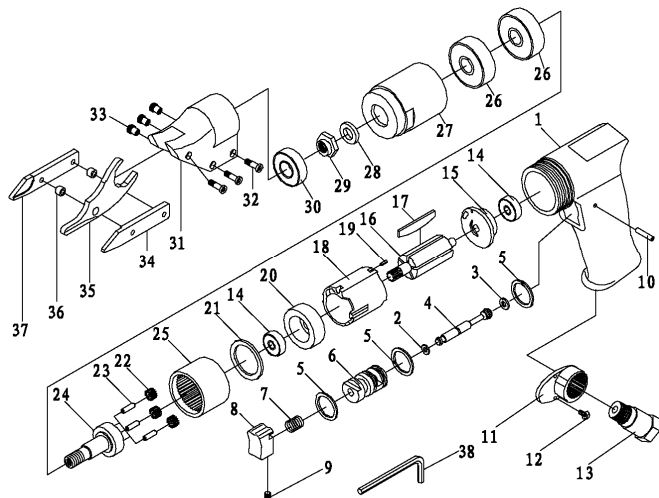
а. Схема устройства и сборки ножницы ручной пневматической MFX 150/006-2.
